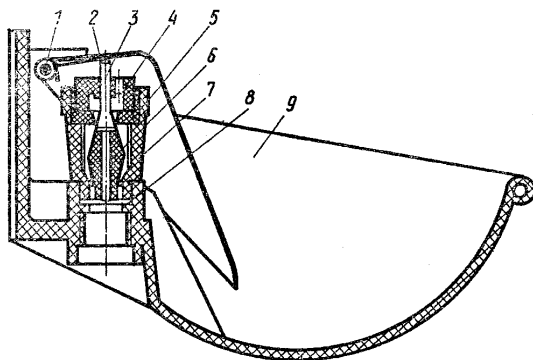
Схема напувалки АП-1А: 1 - вісь; 2 - важіль; 3 - клапан; 4 - прижим; 5 - сидло; 6 - амортизатор; 7 - корпус; 8 - кільце; 9 - чаша
